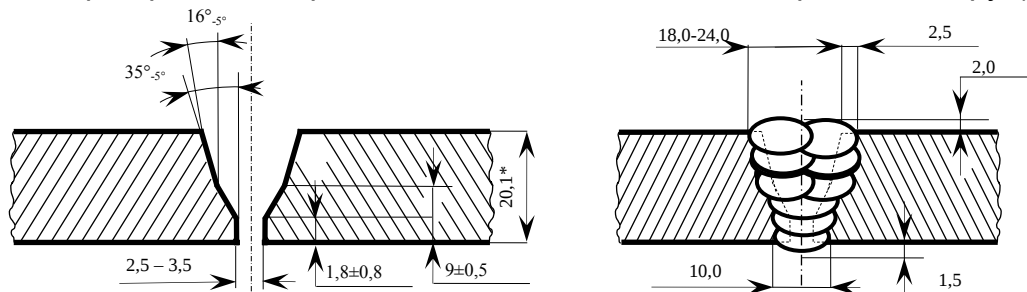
Геометрические параметры сборки и сварного шва КСС №3
